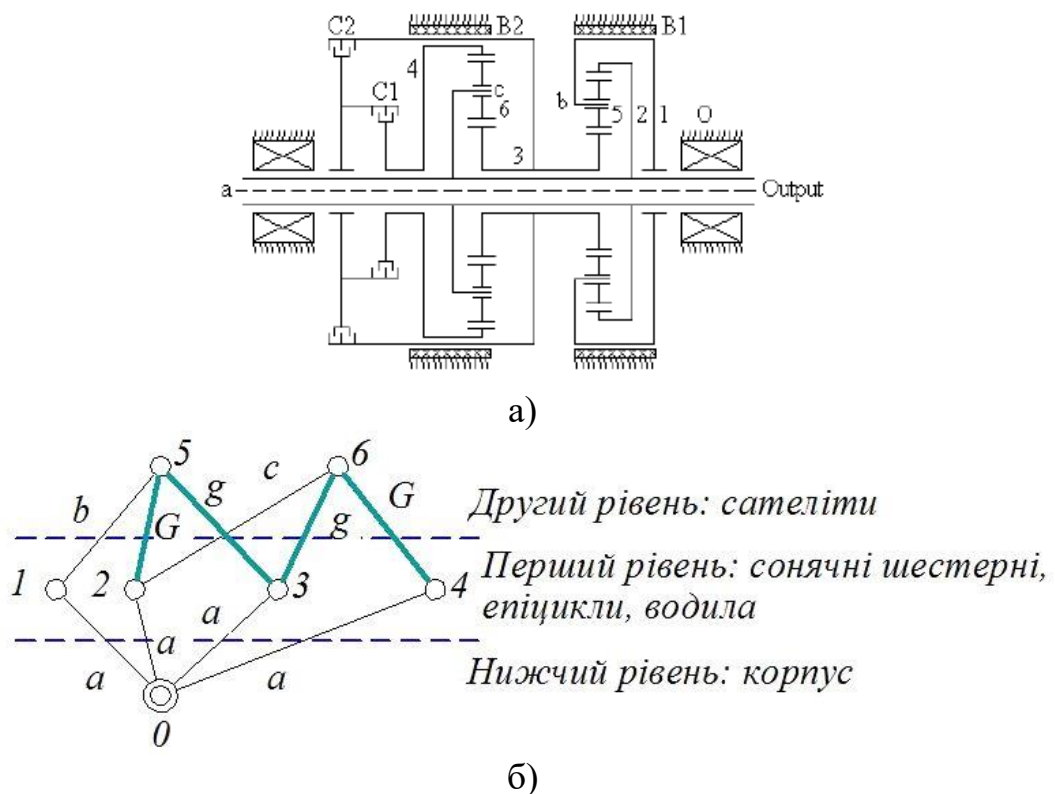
Механічна частина автоматичної коробки передач:
